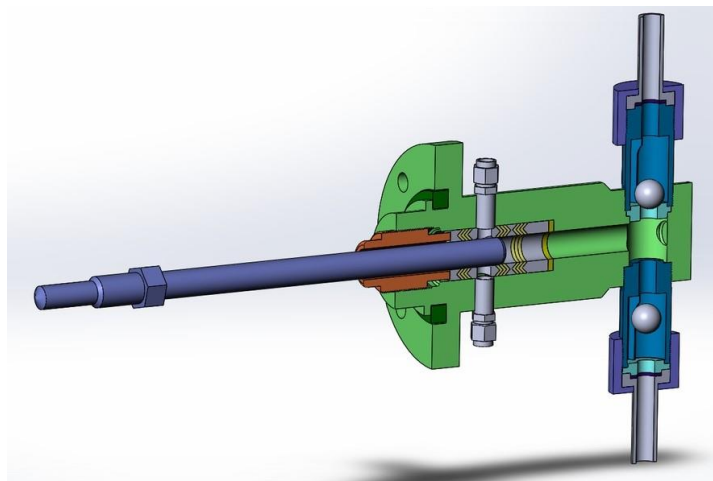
3D-модель гидроблока насосного агрегата типа НД 2,5-40-160
